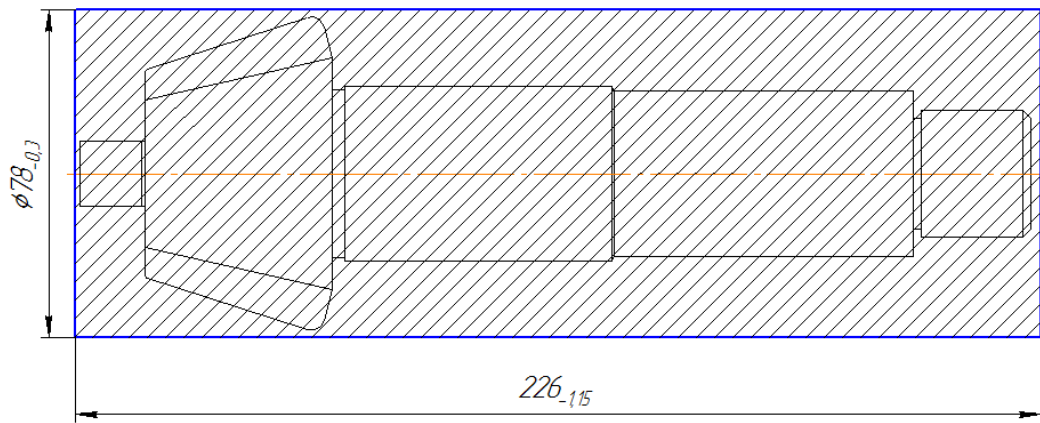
Ескіз заготовки прокат розрізаний різцем
